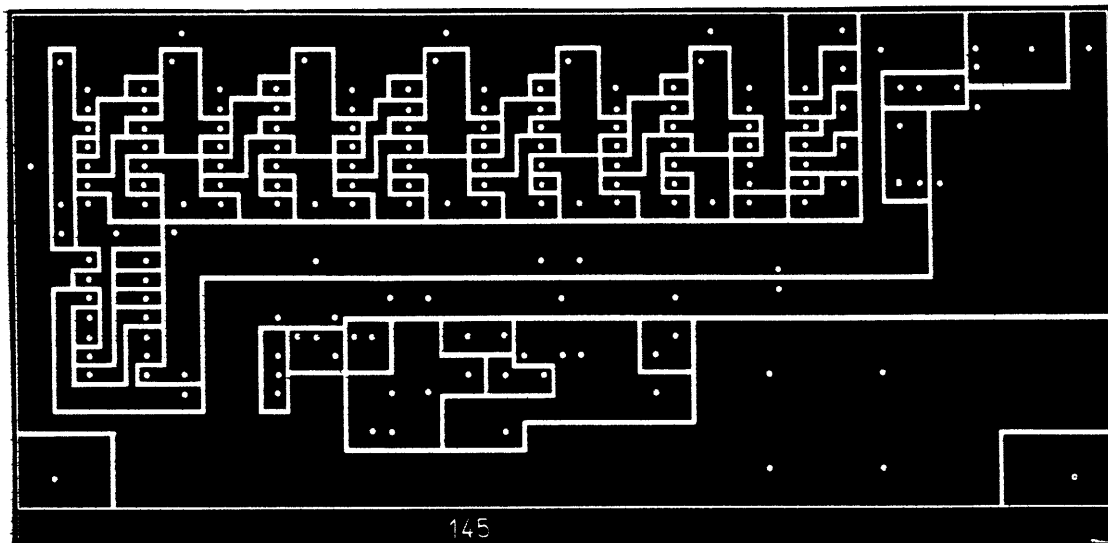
Základní deska univerzální skříňky a chladič IO8
